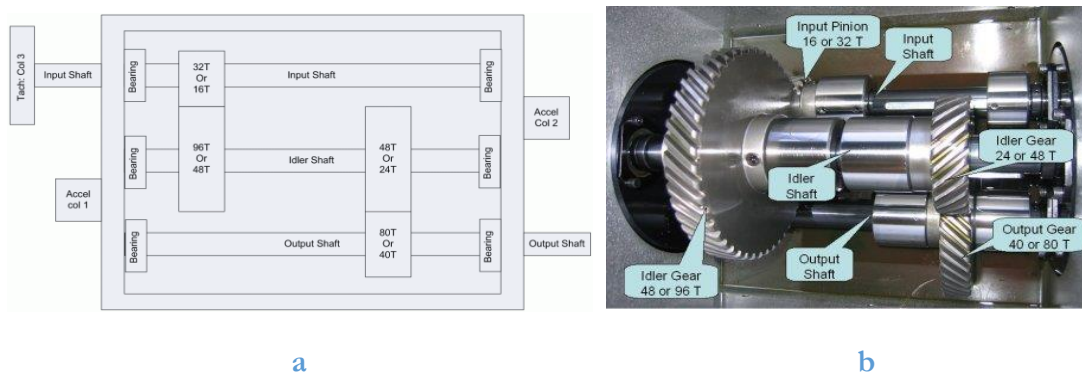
a) Esquema de la caja de engranajes. b) Detalle de la parte interior de la caja de engranajes rectos y helicoidales.
